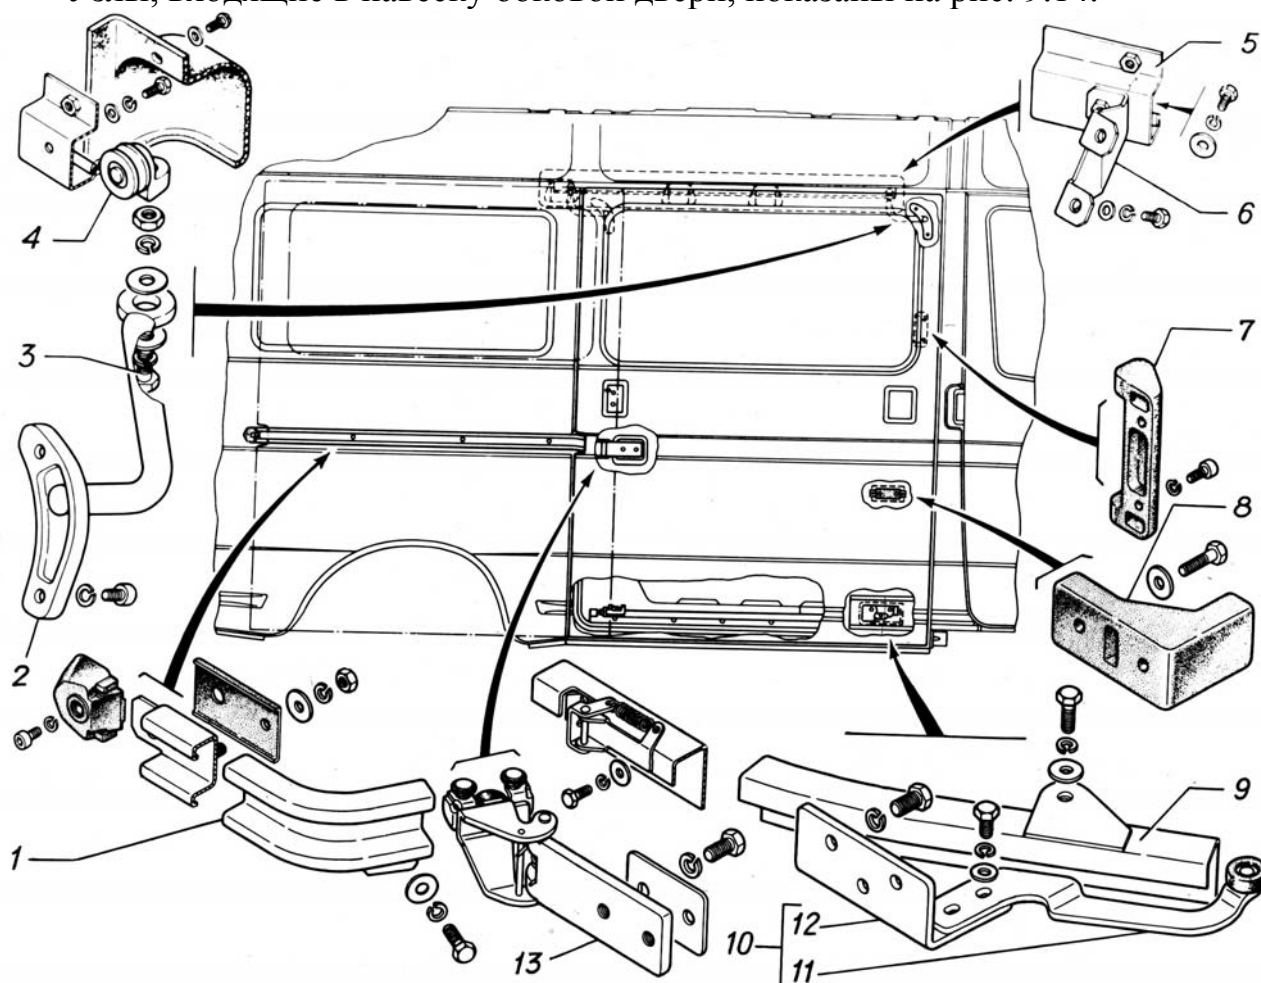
Механизмы перемещения боковой двери: 1 - средняя направляющая; 2 - верхний механизм; 3 - ось верхней каретки; 4 - ролик с кареткой верхнего механизма; 5 - верхняя направляющая; 6 - опора верхней направляющей; 7 - внутренняя ручка; 8 - буфер; 9 - нижняя направляющая; 10 - нижний механизм; 11 - рычаг нижнего механизма; 12 - опора нижнего механизма; 13 - средний механизм
